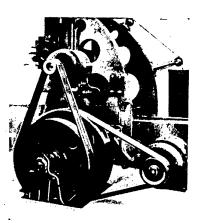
Antrieb einer alten Tischhobelmaschine mit 2 in entgegengesetzter Richtung laufenden Elektromotoren. Umschaltung mit Hilfe elektromagnetischer Vulkankupplungen. (Heid-Billeter, Werkzeugmaschinen GmbH., Bad-Homburg v. d. H.)
